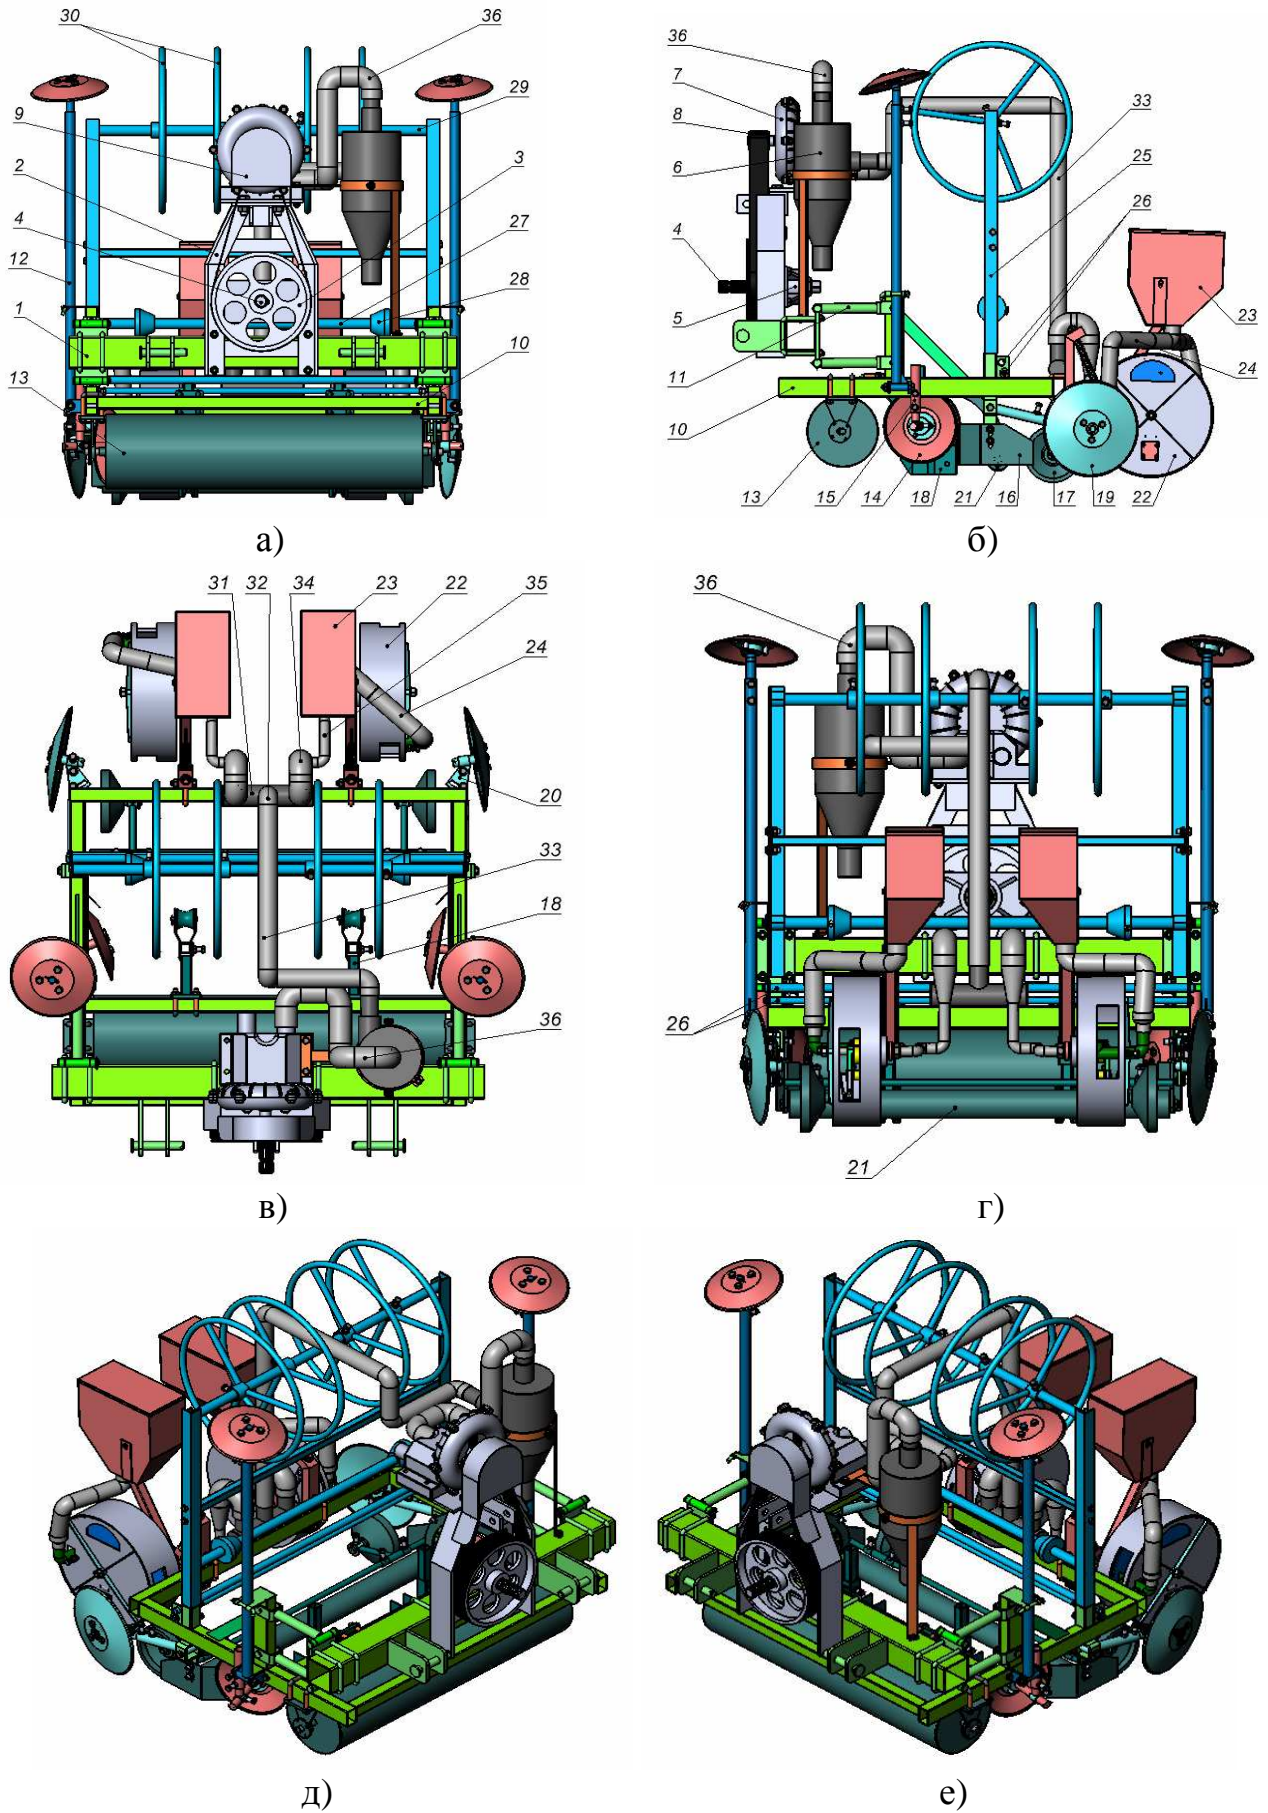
Сеялка для капельного орошения: а) вид спереди; б) вид сбоку; в) вид сверху; г) вид с задней части; д) – общий вид с правой стороны; е) – общий вид с левой стороны
